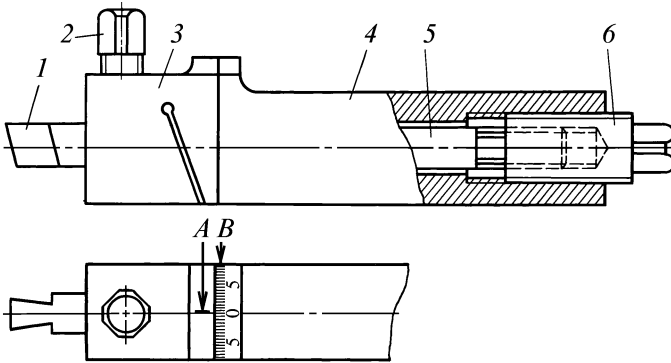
Державка с поворотной головкой для резьбового резца:
